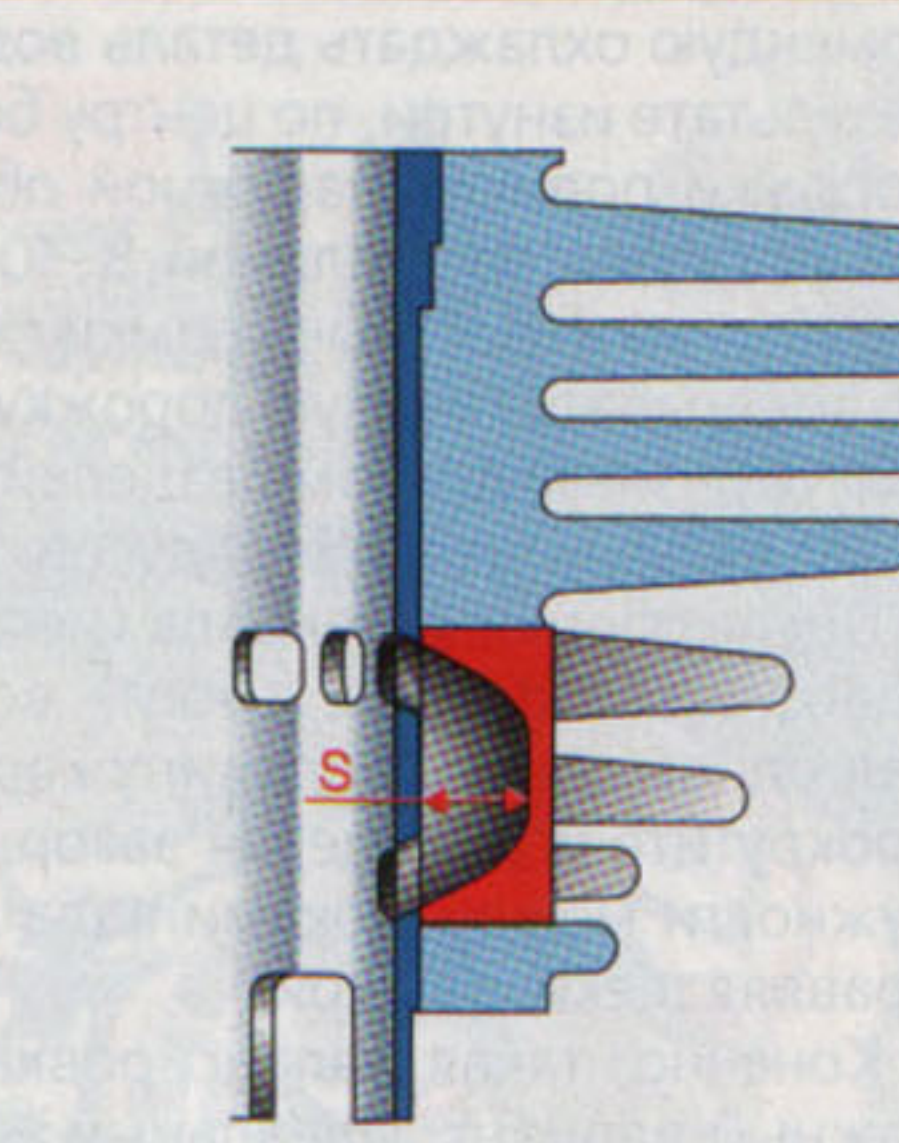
Для формирования дополнительного продувочного канала в рубашке охлаждения фрезеруется площадка, к которой крепится винтами М4 алюминиевая крышка с каналом.
